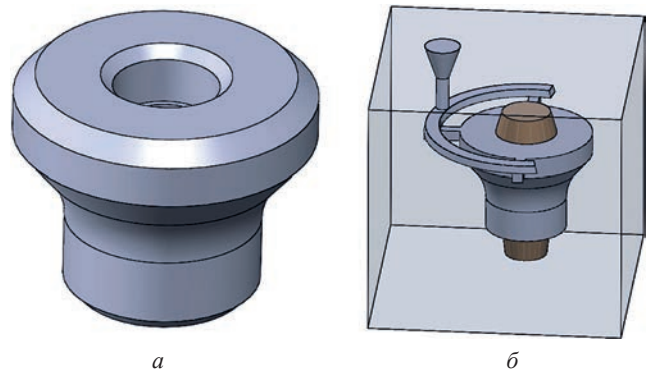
Деталь и отливка: а – деталь «ролик»; б – отливка с литниковой системой
